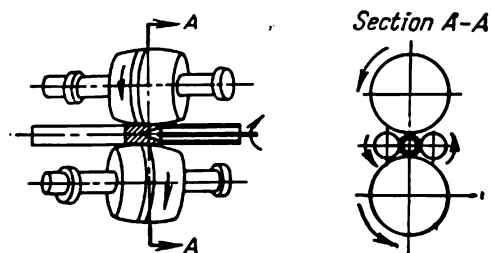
Fabrication des tubes sur des bancs pousseurs à cylindres
